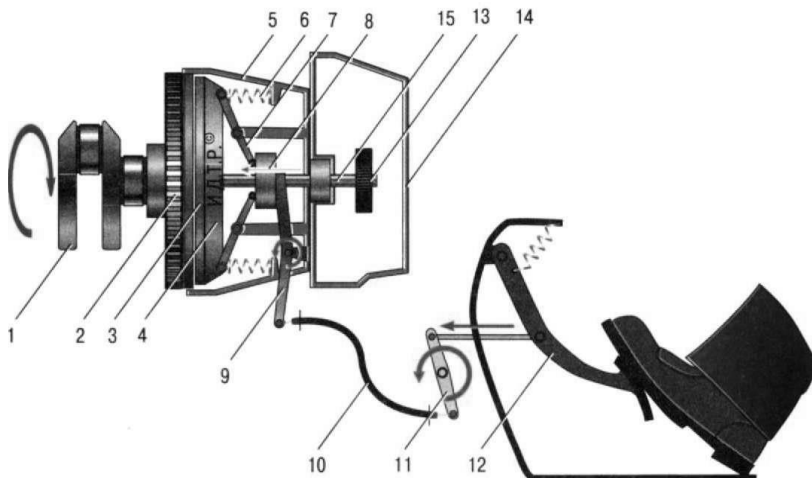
Схема механического привода выключения и механизма сцепления: 1 - коленчатый вал; 2 - маховик; 3 - ведомый диск; 4 - нажимной диск; 5 - кожух сцепления; 6 - нажимные пружины; 7 - отжимные рычаги; 8 - подшипник выключения сцепления; 9 - вилка выключения сцепления; 10 - металлический трос; 11 - рычаг привода; 12 - педаль сцепления; 13 - шестерня первичного вала; 14 - картер коробки передач; 15 - первичный вал коробки передач
